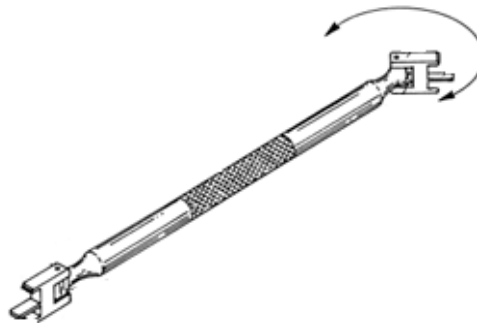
Posicionador com dupla face e elementos rotatórios.
